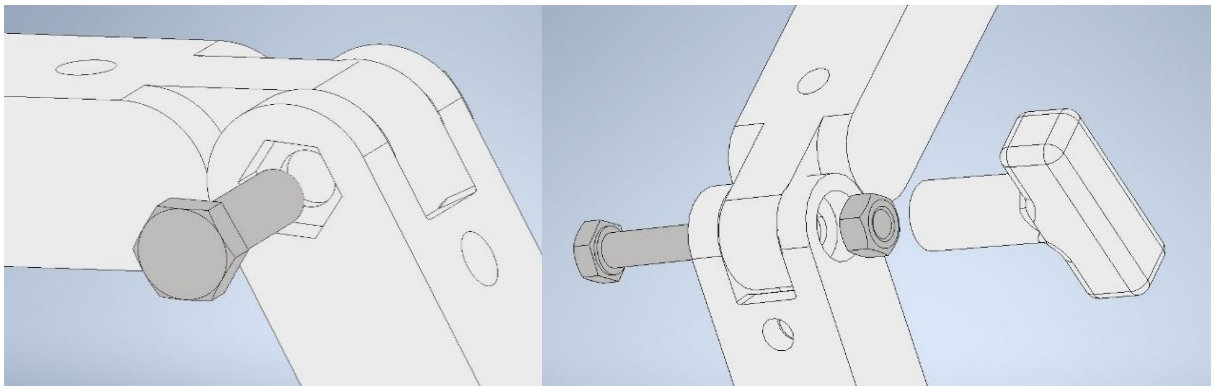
Detailansichten des Klemmgelenks mit eingelassener Sechskantschraube und Mutter
